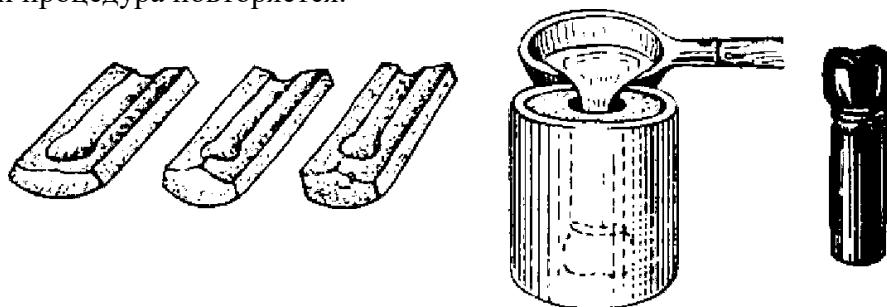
Сопоставление частей гипсового блока и отливка штампа из легкоплавкого сплава.
